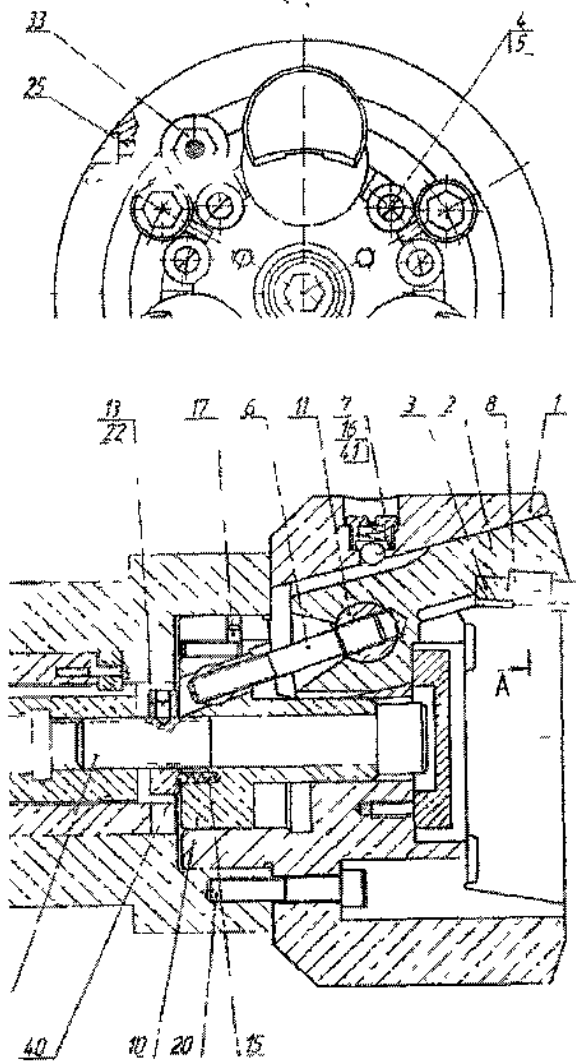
Штоковий 3-кулачковий патрон для затиску по необробленій поверхні
